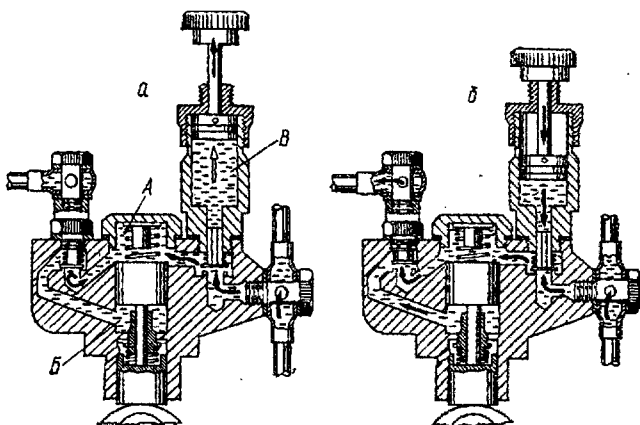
Схема действия топливоподкачивающего насоса при ручном приводе: а – подготовительный ход; б – рабочий ход; А и Б – соответственно надпоршневая и подпоршневая полости подкачивающего насоса; В – полость цилиндра насоса ручной подкачки топлива
